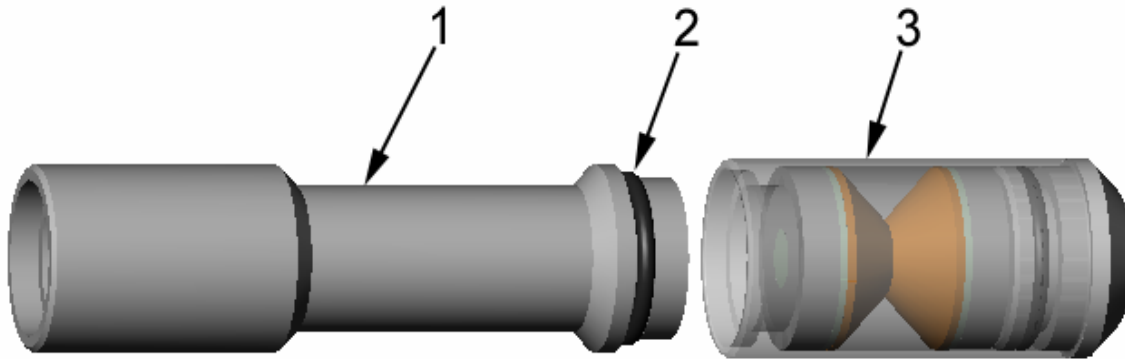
Vue éclatée, dimensions 1,156 po (29,36 mm) - 1,460 po (37,08 mm)
